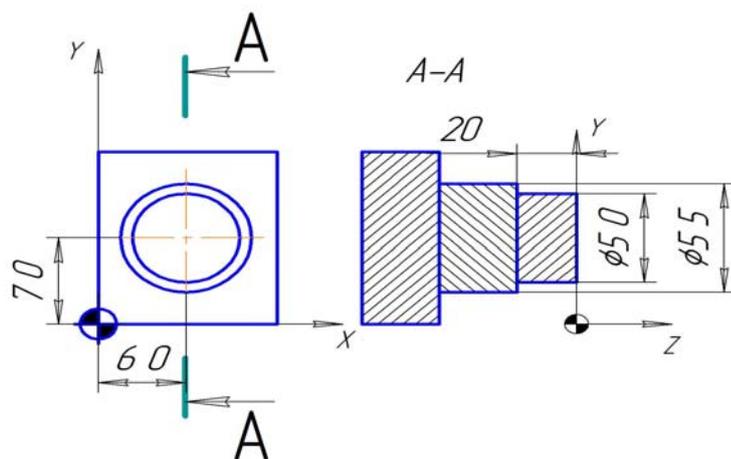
Круговой выступ, обрабатываемый с использованием цикла CYCLE77
